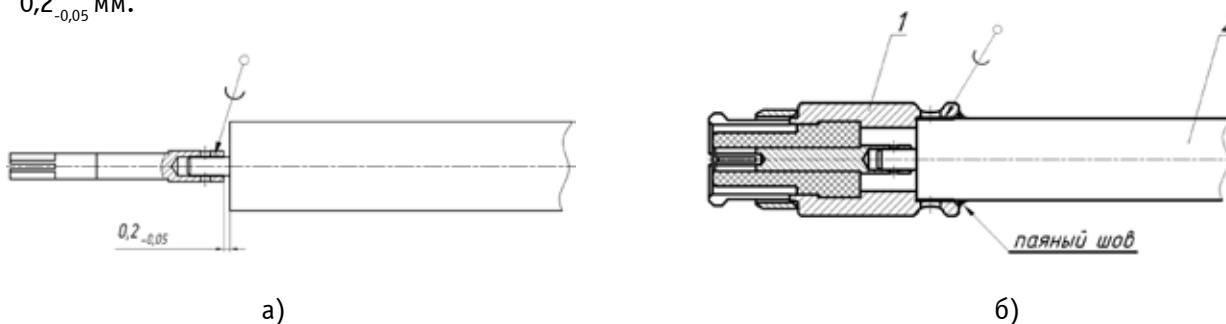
Пайка гнезда на жилу (а) и установка корпуса на кабель (б)
